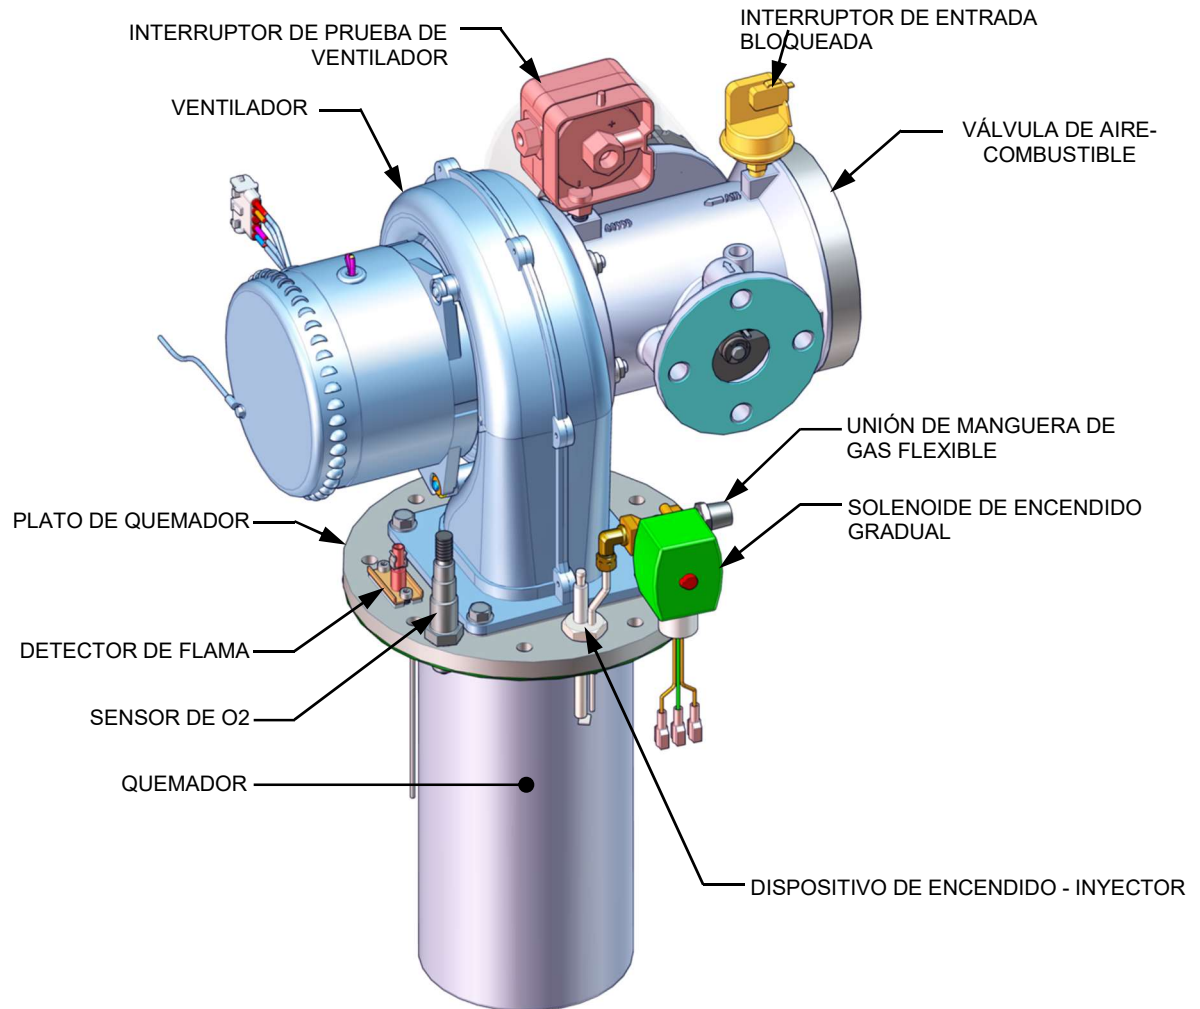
Ensamblado del quemador de BMK 750/1000 (retirado de la caldera)
